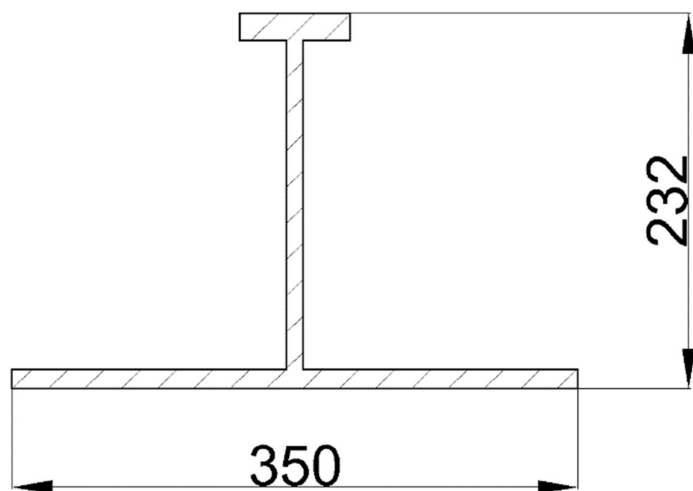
Наближений переріз профілю шпангоута з приєднаним пояском для варіанта конструкції борту з подовженими проміжними шпангоутами і посиленими бортовим стрингером
